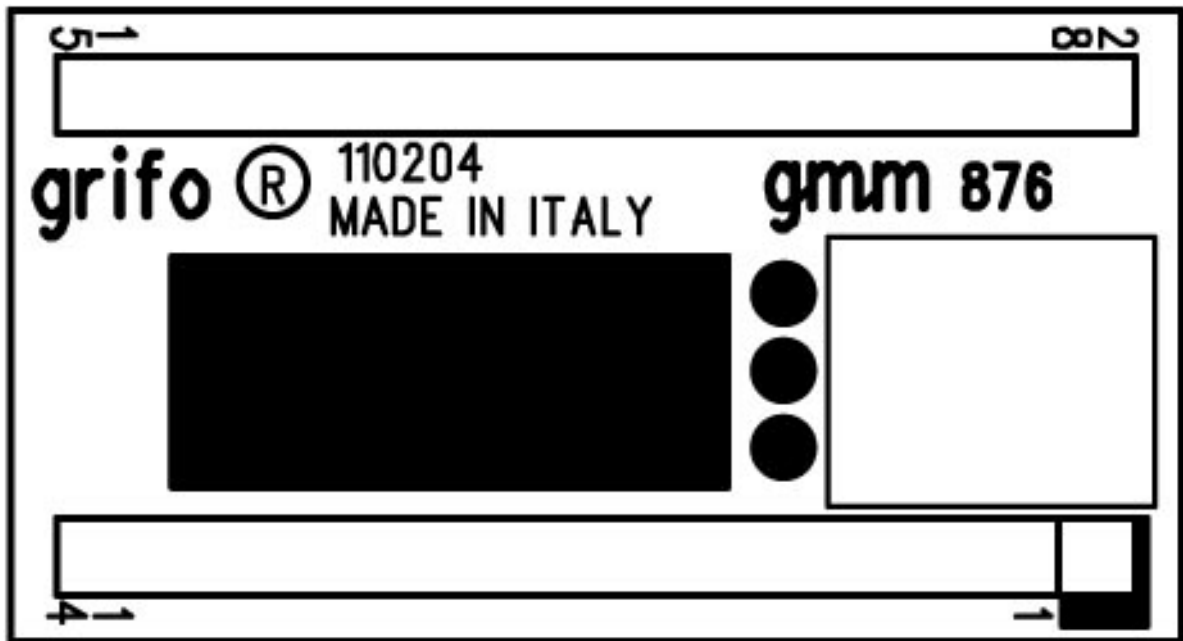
PIANTA COMPONENTI - VISTA LATO SALDATURA
